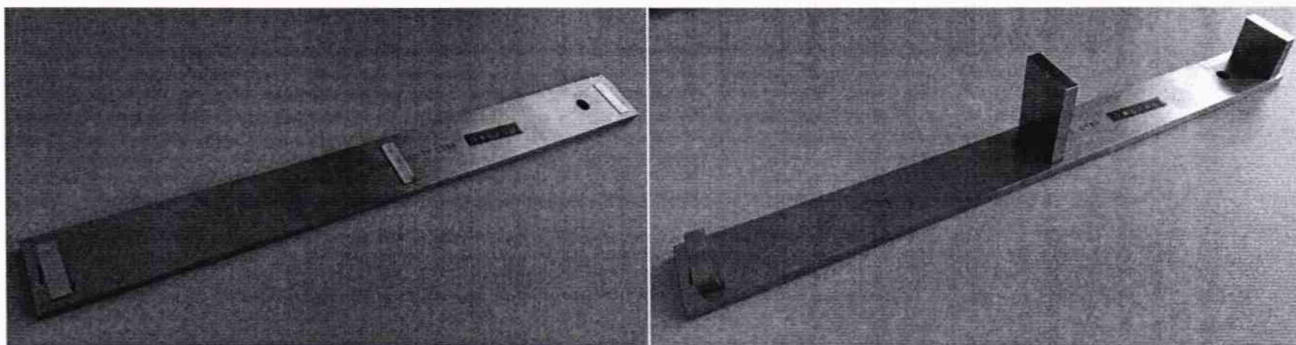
Установка концевых мер на рабочую поверхность линейки поверочной
